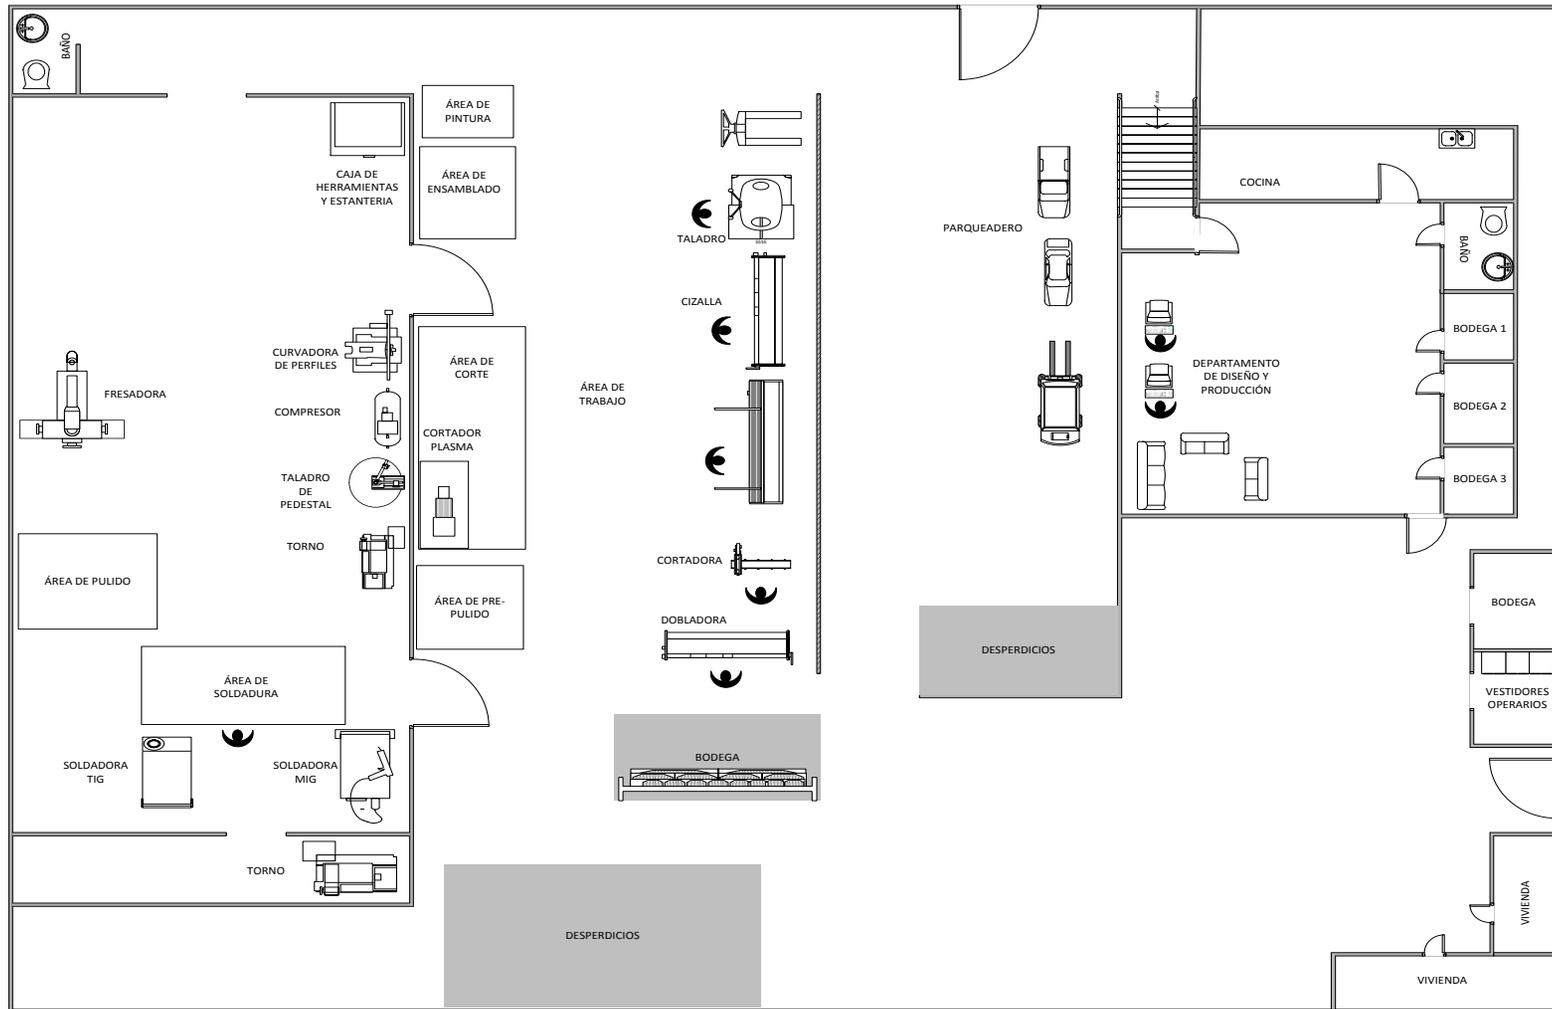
Diseño de Planta de la Empresa INDUMEI
